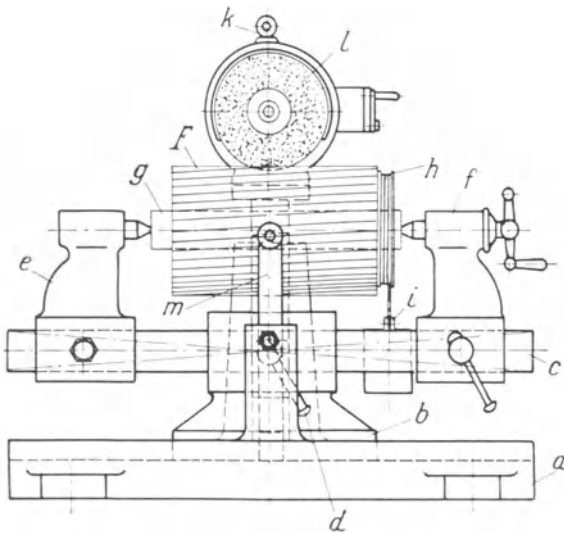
Schleifvorrichtung für große spiralgenutete Fräser.
